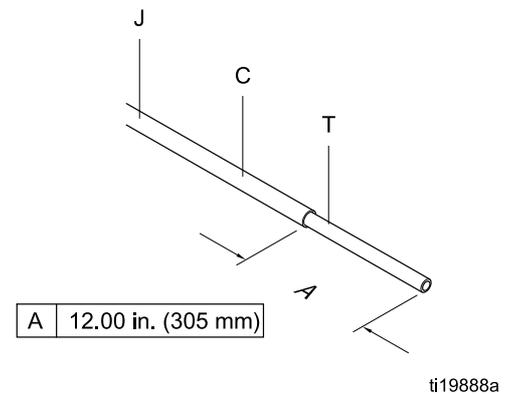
Abmessungen am WB100-Gehäuse für ungeschirmten Schlauch 24M733
